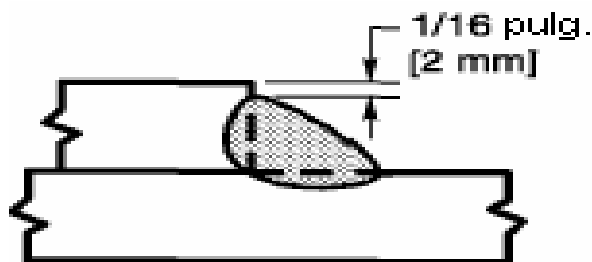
Traslape de Soldaduras Tipo Filete
